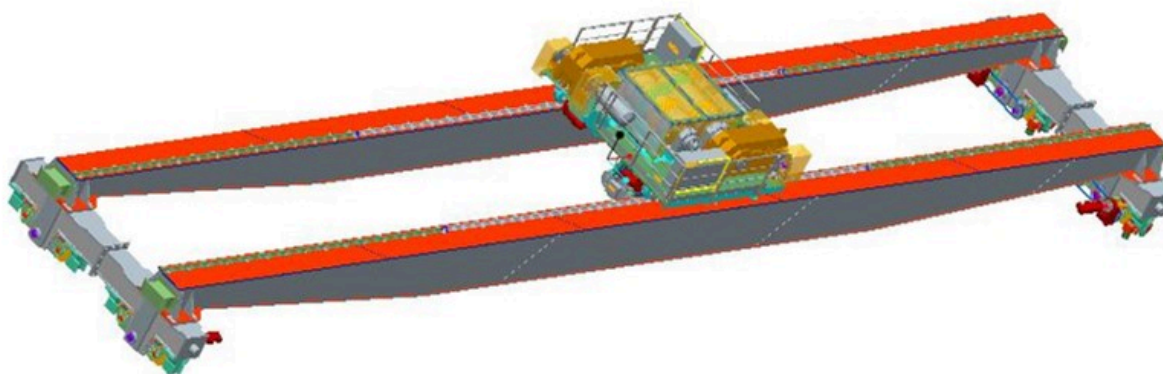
Pont du Hall d'Entreposage [X]
